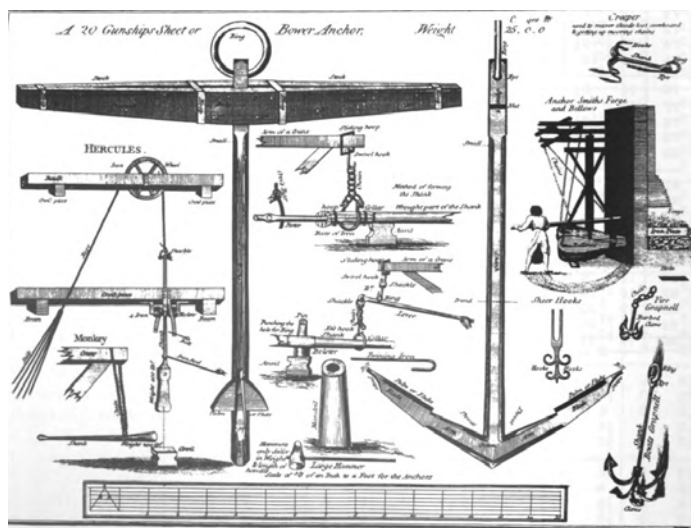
Âncora central do tipo “Old Plan Long Shank”(Curryer,1999).
